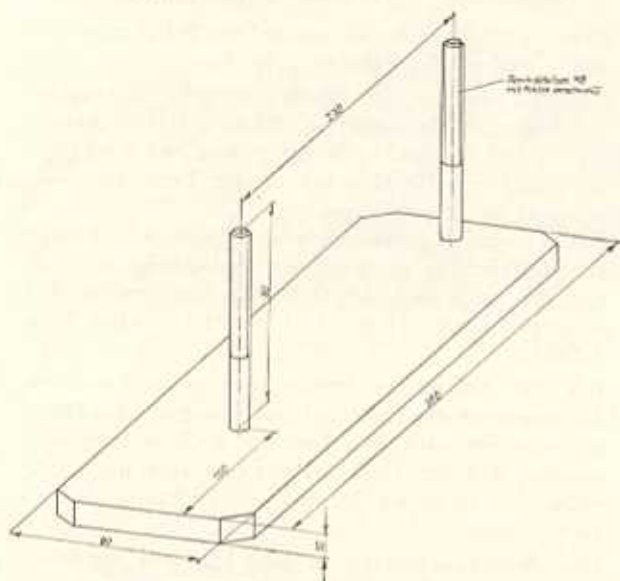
Haltevorrichtung für Lenkgetriebe (Maßskizze)
